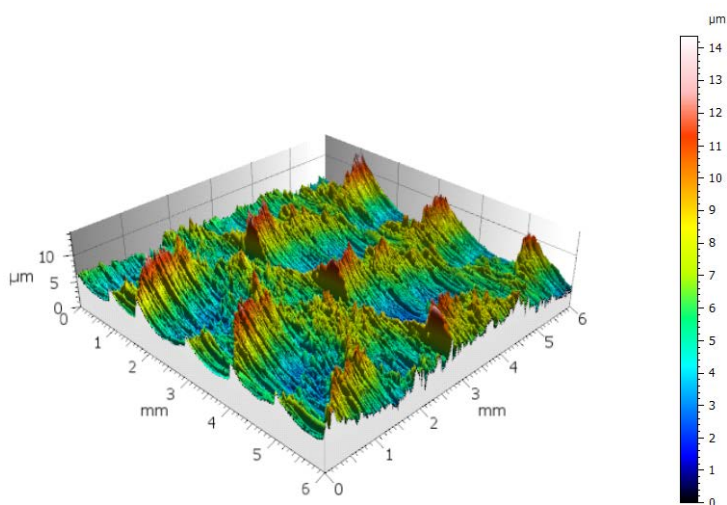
Топографія обробленої поверхні після фрикційної обробки інструментом з гладкою поверхнею
